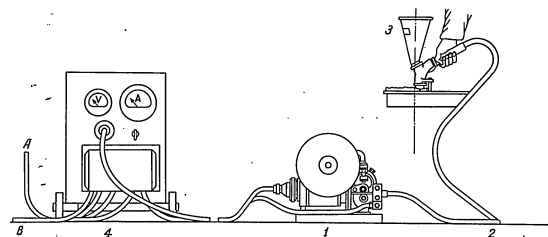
Схема шлангового полуавтомата ППШ-5:
